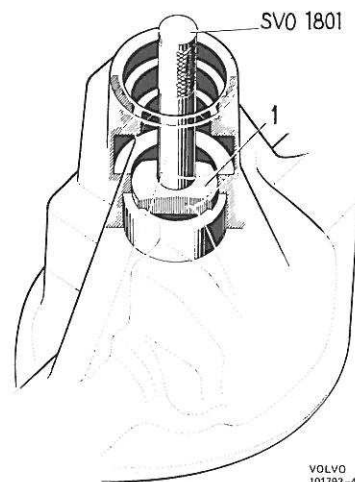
Démontage de la cuvette de roulement arrière de pignon
